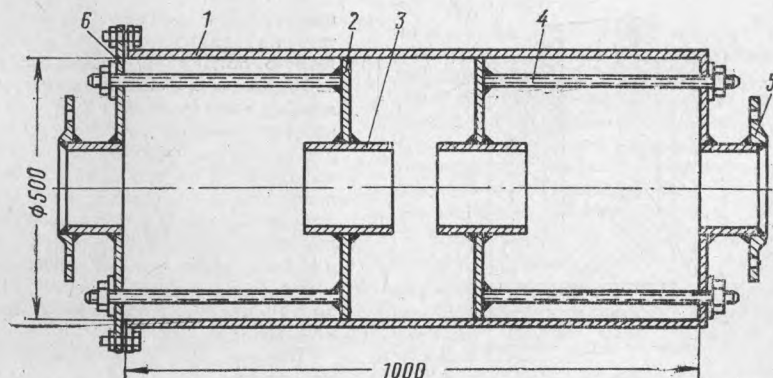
Реактивный глушитель шума компрессоров с передвижными диафрагмами:
